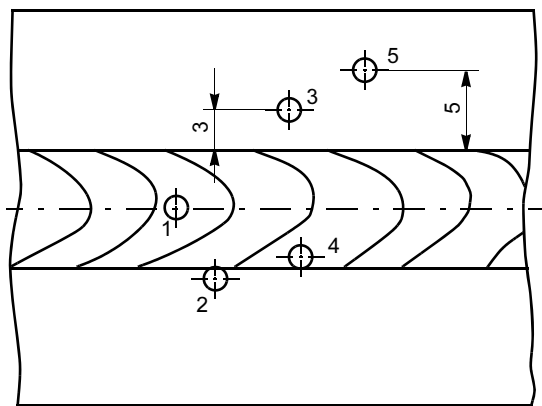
Точки 1—5 замера напряжений в сварном соединении
